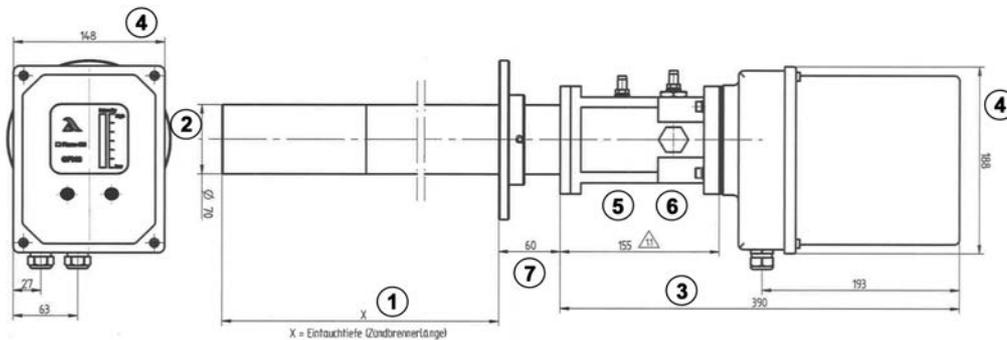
Dimensiones del quemador de ignición GFI70, variante A/B
